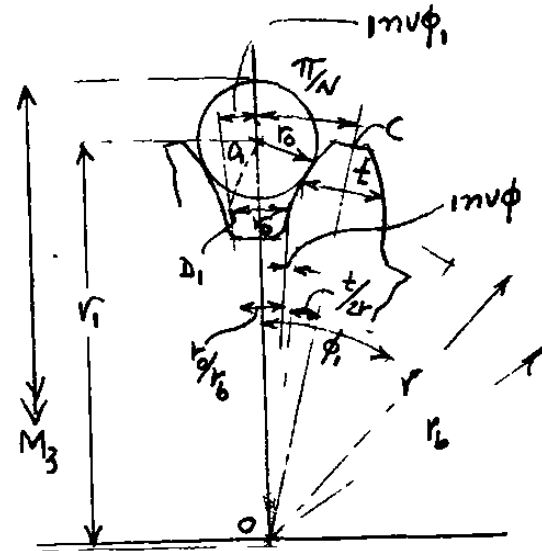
Espesor del diente por medición sobre rodillos para un No. par de dientes.
